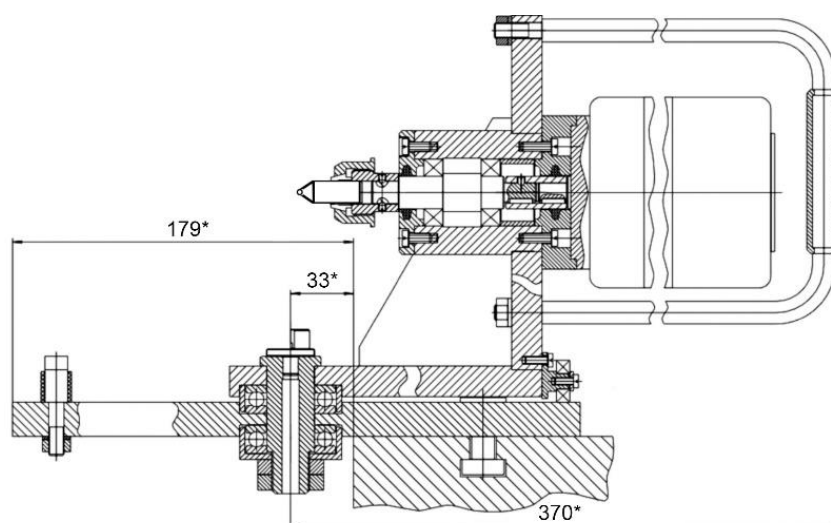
Поворотное устройство для формирования сферической формы рабочей части наконечника
